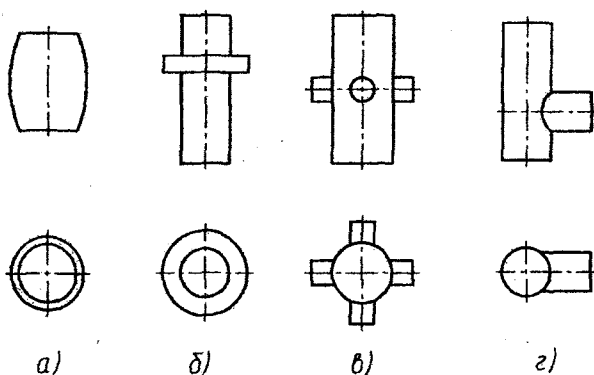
Типовые поковки, изготавливаемые выдавливанием в разъемную матрицу: а) для роликов подшипников; б) типа шестерен; в) типа крестовин; г) типа фитингов трубопровода
